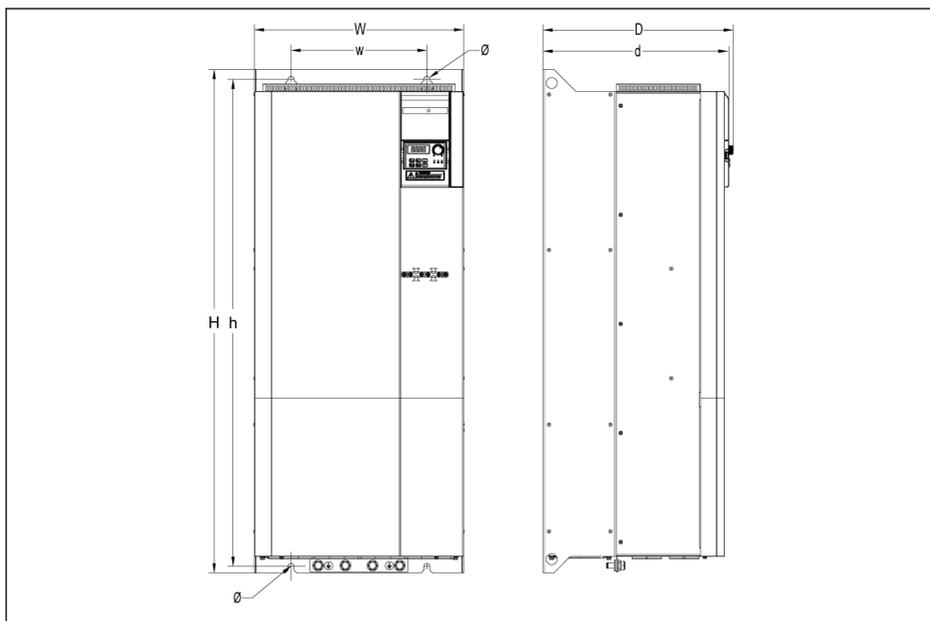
Imagen de dimensiones de EFC 5610 110K...132K
